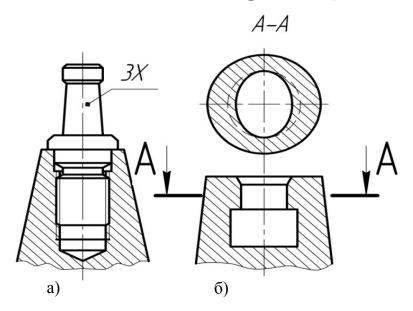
Захват, ввернутый в хвостовик режущего инструмента
